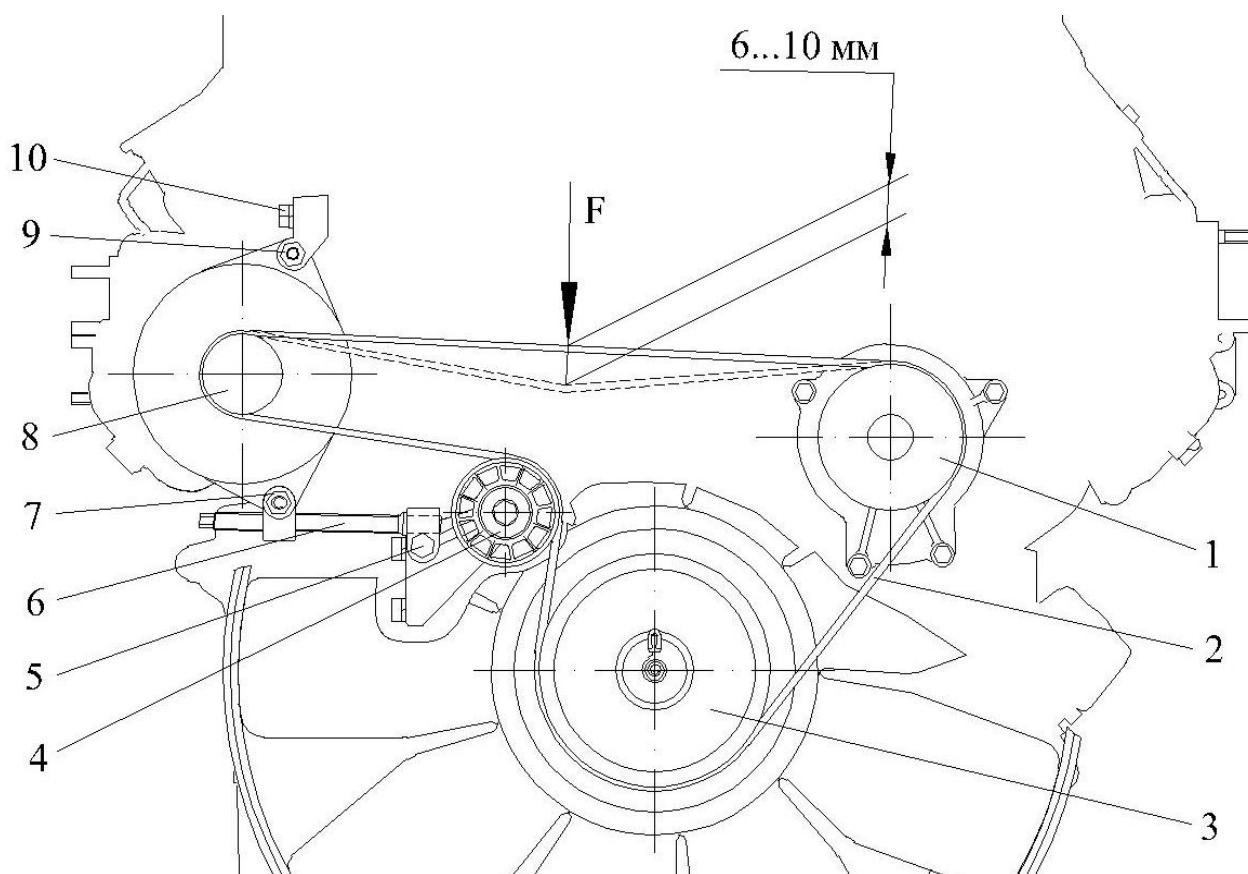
Схема проверки натяжения ремня привода генератора и водяного насоса:
